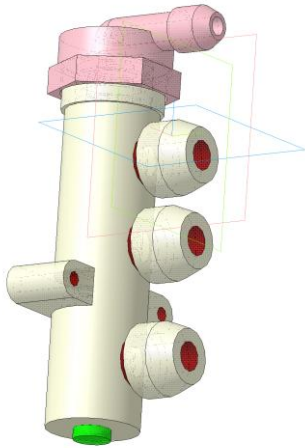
Пример сборочного чертежа (клапан редукционный)
